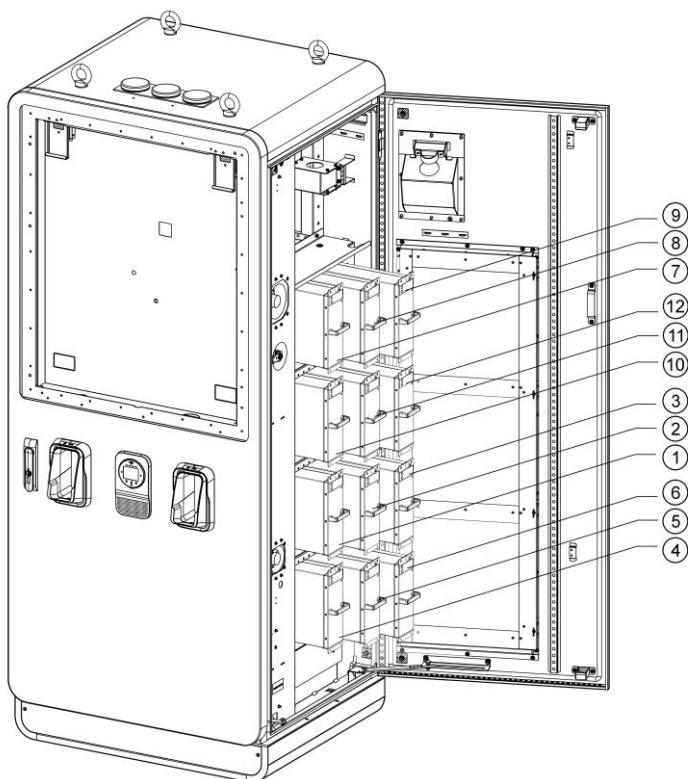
Installera laddningsmodulerna (för MaxiCharger DC 120)
